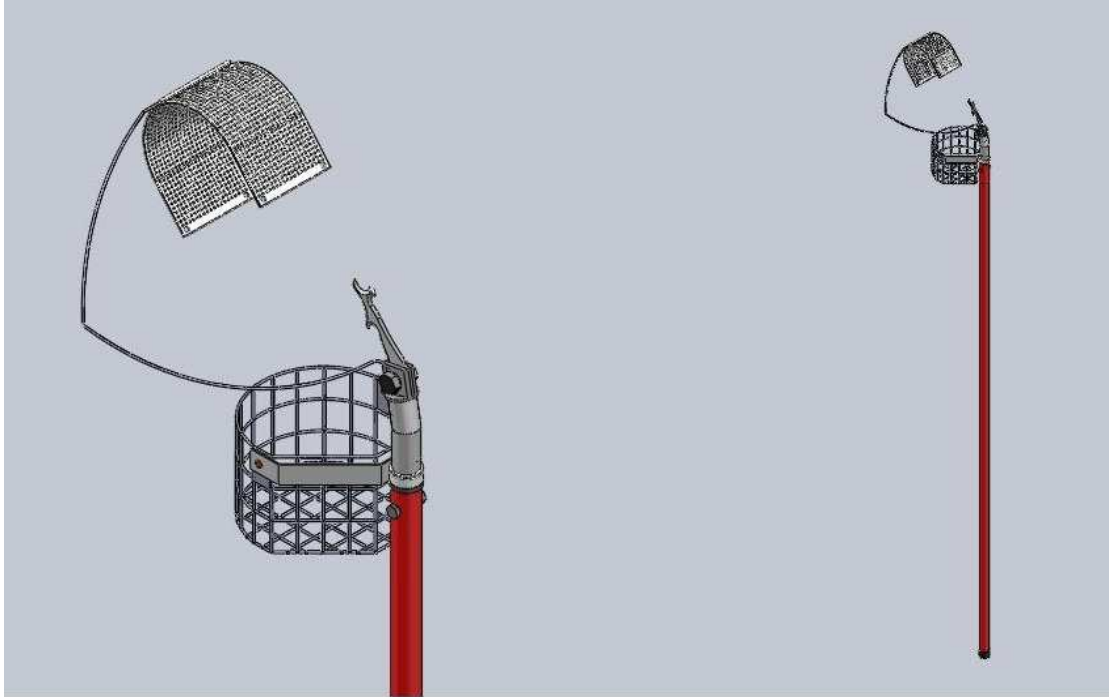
Diseño del cortador de la alternativa seleccionada. Fuente: El Tesista.
